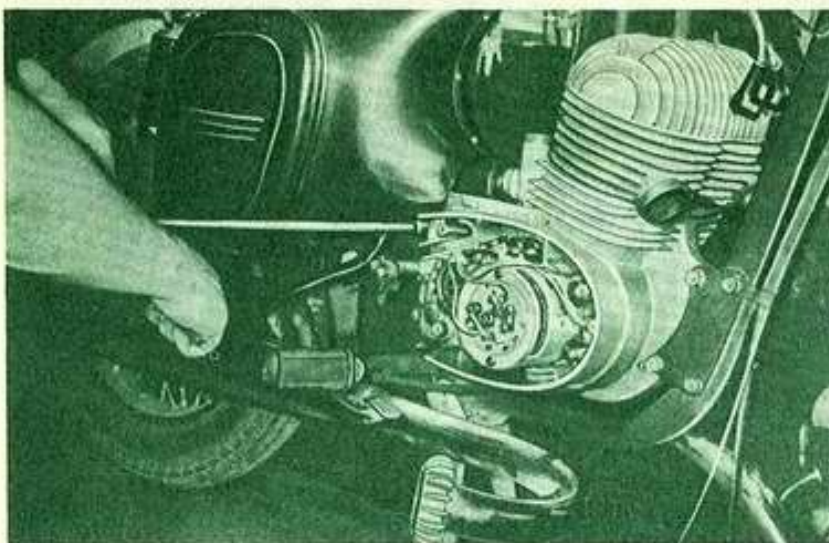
Вывертывание торцовым ключом задних болтов крепления двигателя
